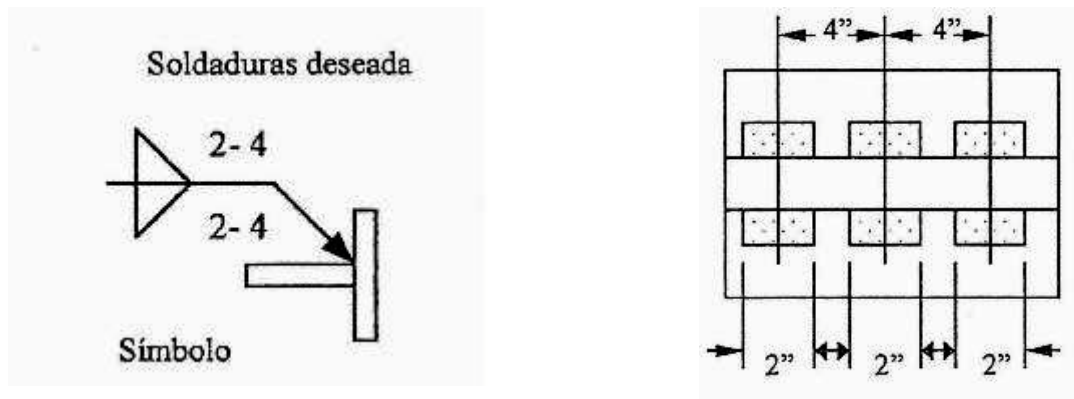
SOLDADURAS DE FILETE INTERMITENTE EN CADENA.
